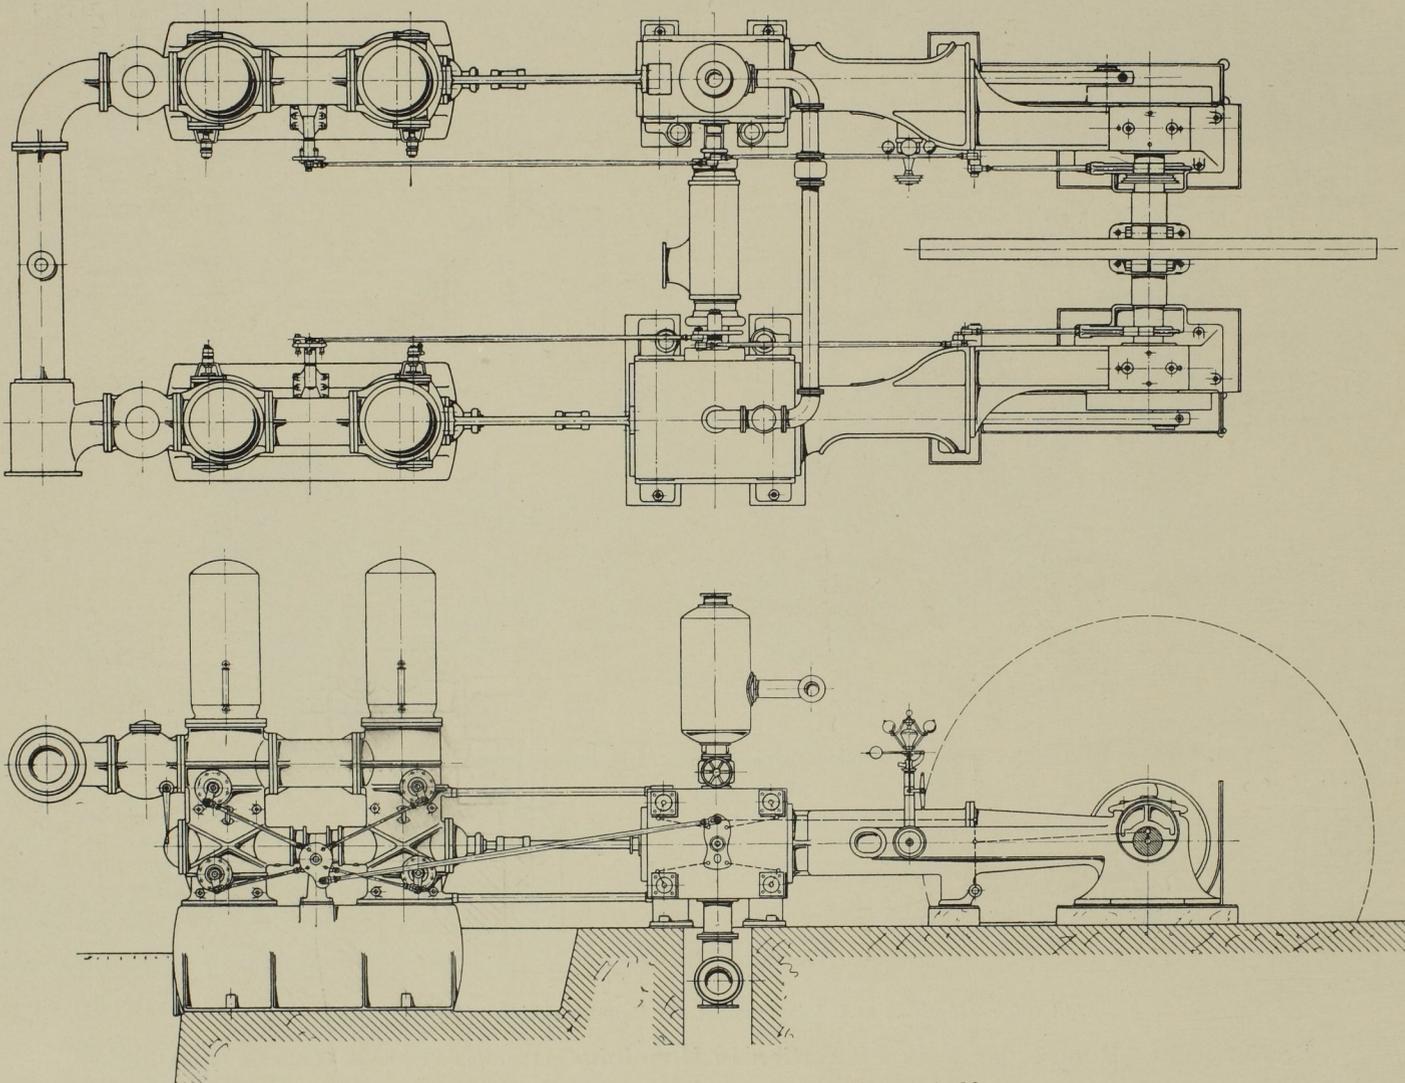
Grundriss und Seitenansicht. Massst. 1:96.
